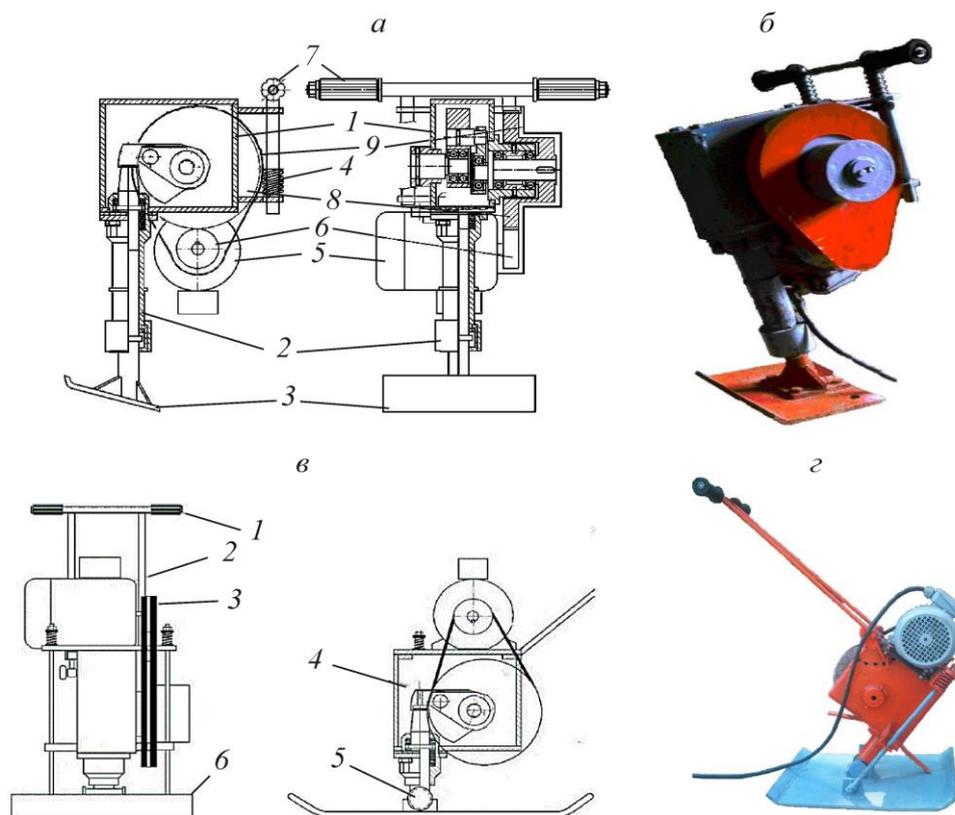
Общий вид опытного образца механической трамбовки МТ-2 и виброплиты ВП-2 с МПС (а): 1 — корпус ударного узла; 2 — букса; 3 —трамбующий башмак; 4 — виброгаситель рукоятки; 5 — электродвигатель; б — шестерня; 7 — рукоятка управления; 8 — зубчатое колесо; 9 — кожух редуктора; б — ручная трамбовка МТ-2 с МПС; в — виброплита ВП-2: 1 — рукоятка управления; 2 — приводной электродвигатель; 3 — клиноременная передача; 4 — ударный механизм; 5 — поворачивающий шарнир, обеспечивающий регулирование наклона ударного узла машины; б —трамбующая плита; г — ручная виброплита ВП-1 с МПС
